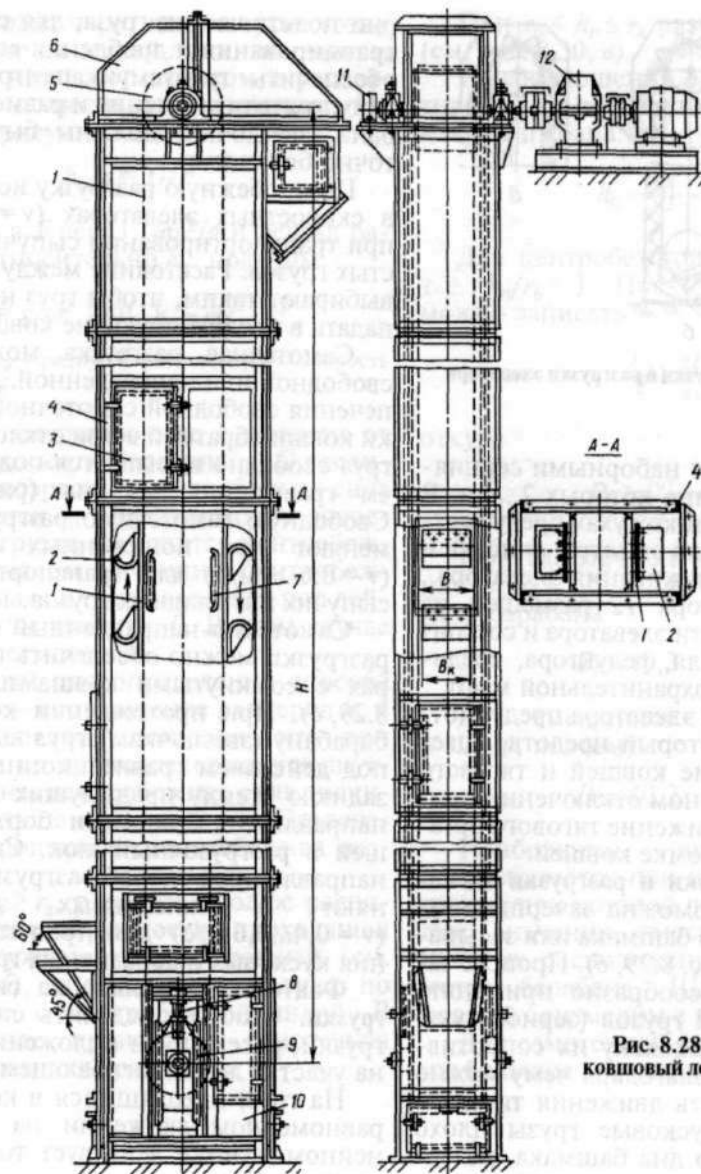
Вертикальный ковшовый ленточный элеватор
